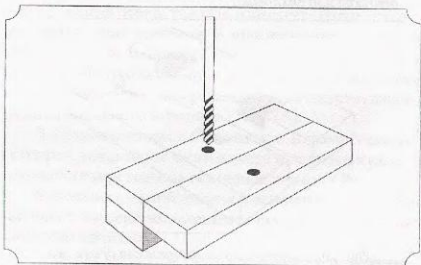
В верхней части заготовки, не разрезая ее, сверлят сквозные отверстия под дополнительный штырь (скрепляющие верхнюю и нижнюю части). Соединяют части и, используя одно из этих отверстий в качестве направляющего, в нижней части заготовки сверлят отверстие для установки соответствующего дополнительного штырька
